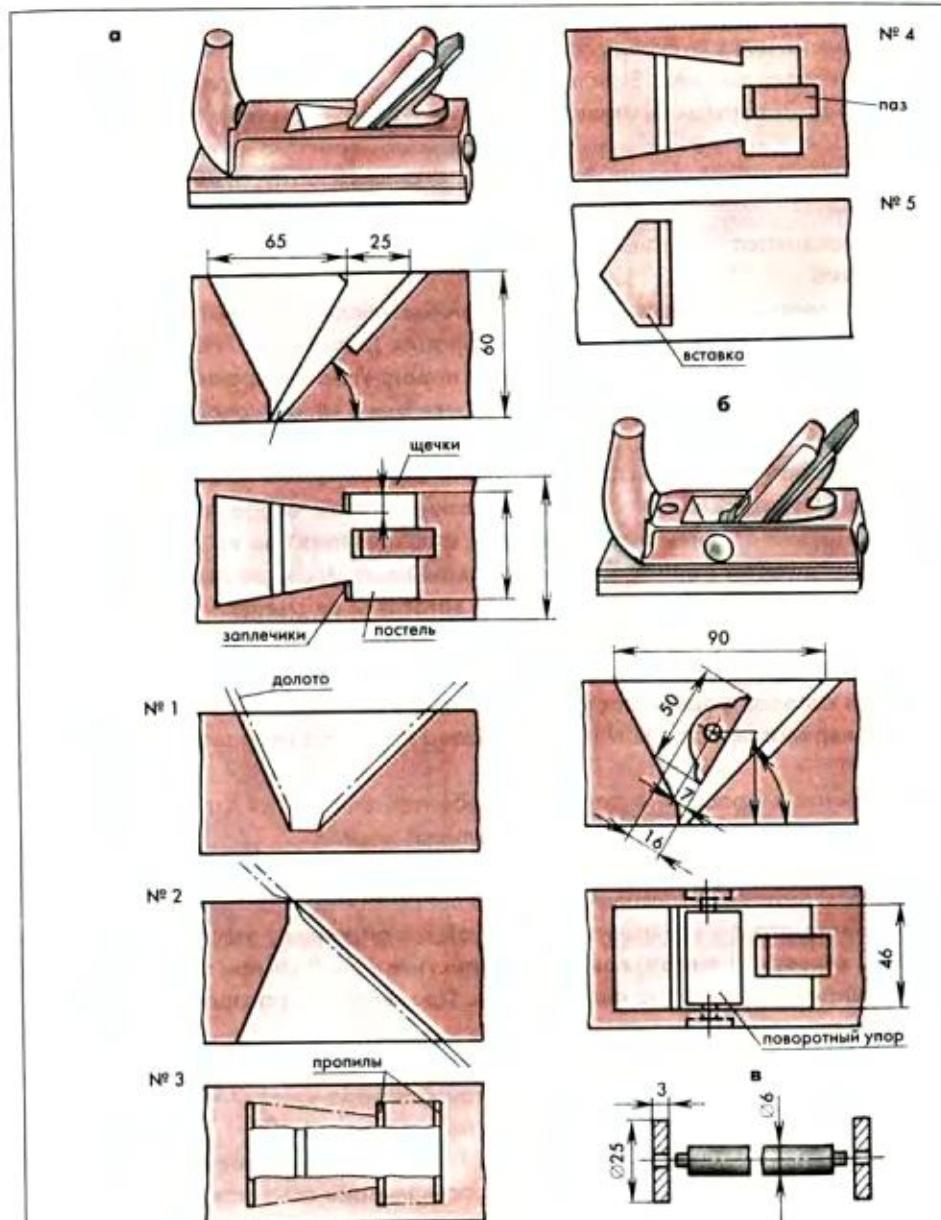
Операции изготовления рубанков с прямым двойным ножом:
